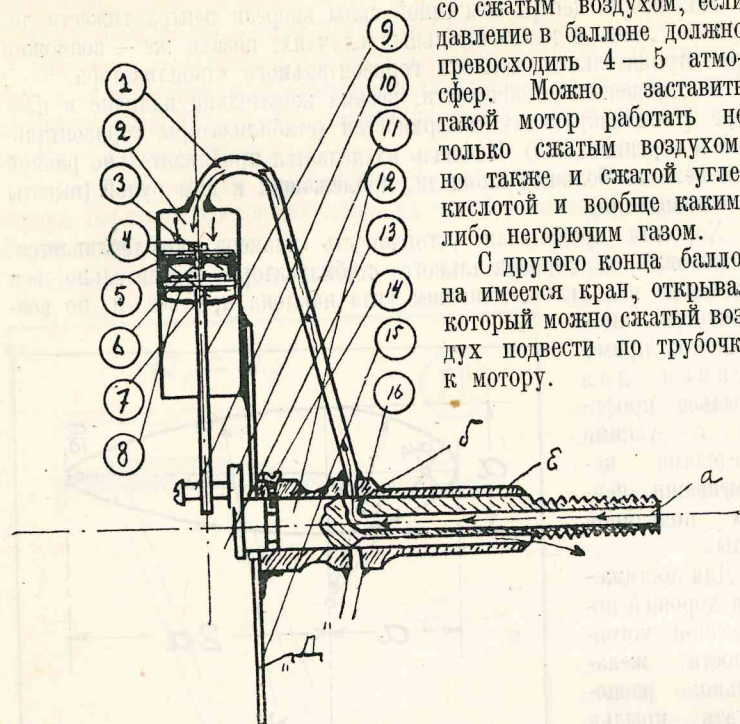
а. Разрез двигателя: 1 — трубочка, подводящая сжатый воздух к цилиндру; 2 — цилиндр; 3 — поршень; 4 — винт, удерживающий шайбу; 5 — шайба; 6 — донце поршня; 7 — палец поршневой; 8 — вкладыш; 9 — шатун; 10 — палец кривошипа; 11 — тело кривошипа; 12 — вал; 13 — винт стопорный кривошипа; 14 — винт стопорный вала; 15 — диск с цилиндрами; 16 — втулка распределителя.
